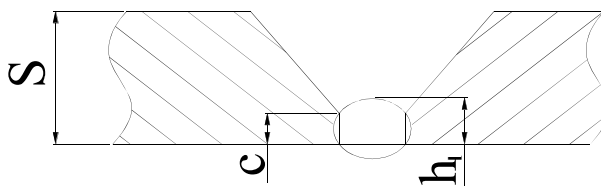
Первый проход при односторонней сварке.
